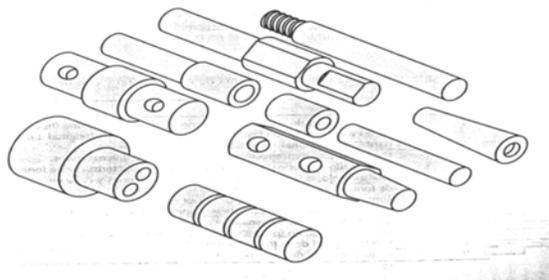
Diez partes diferentes en tamaño y forma, pero muy similares en términos de manufactura. Todas las partes se maquinan con torneado a partir de materia prima cilíndrica; algunas partes requieren taladrado o fresado.
